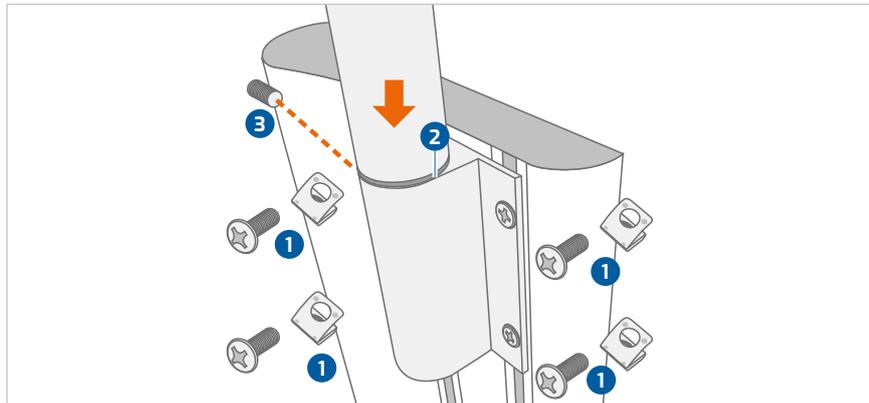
Montare il braccio telescopico sul carrello del dispositivo
